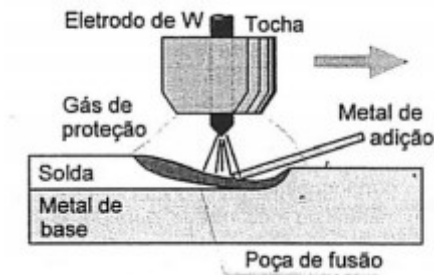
Desenho esquemático da soldagem GTAW. [13]
